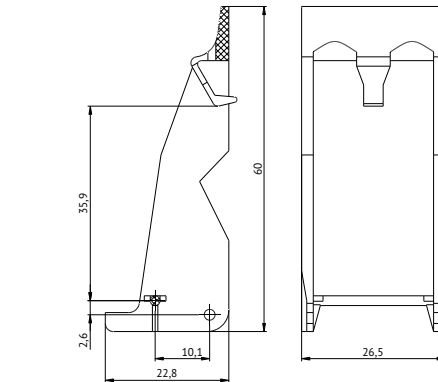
Габаритные, установочные присоединительные размеры фиксатора реле OptiRel 55-H4
